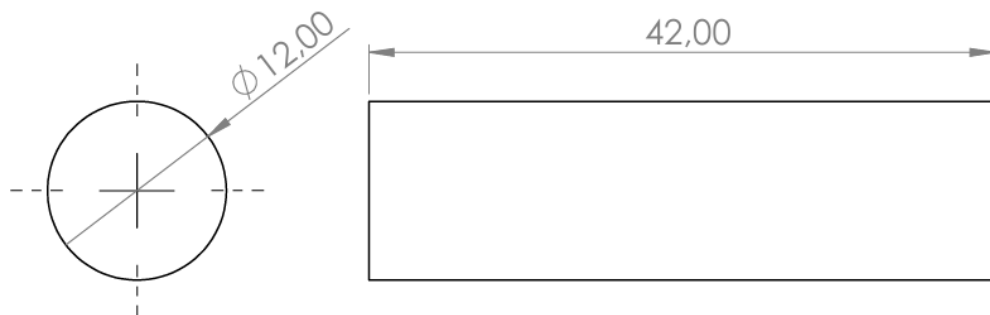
Заготовка у вигляді циліндричного прута
